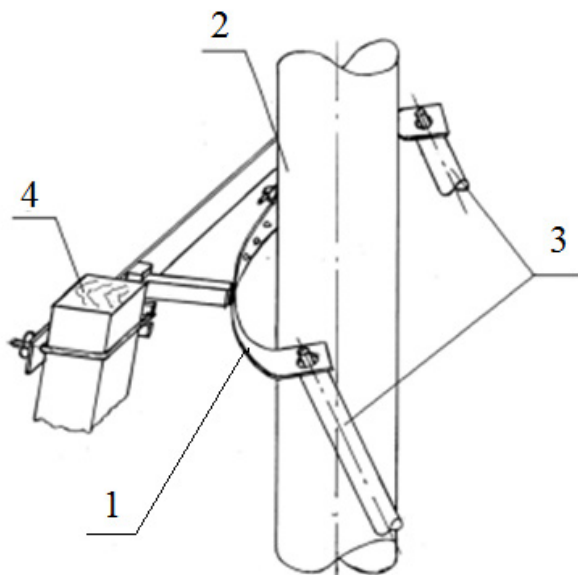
Схема насадка на лестницу для подъема на неустойчивые опоры с опорными штангами (пояснения в тексте)
